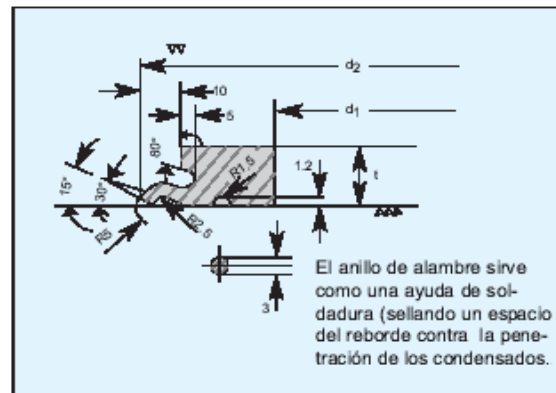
Juntas de sellado anillo de soldadura.
